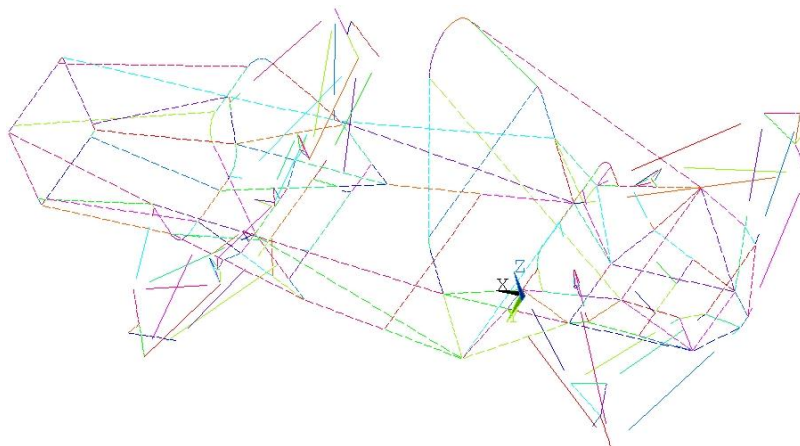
Prutový model rám v programu Pro/Engineer WF5
